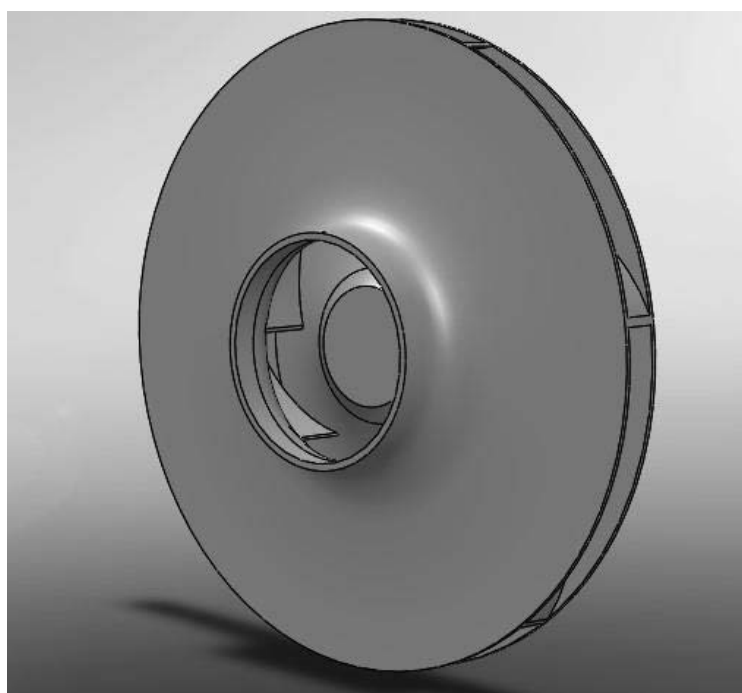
3D-модель рабочего колеса центробежного насоса
